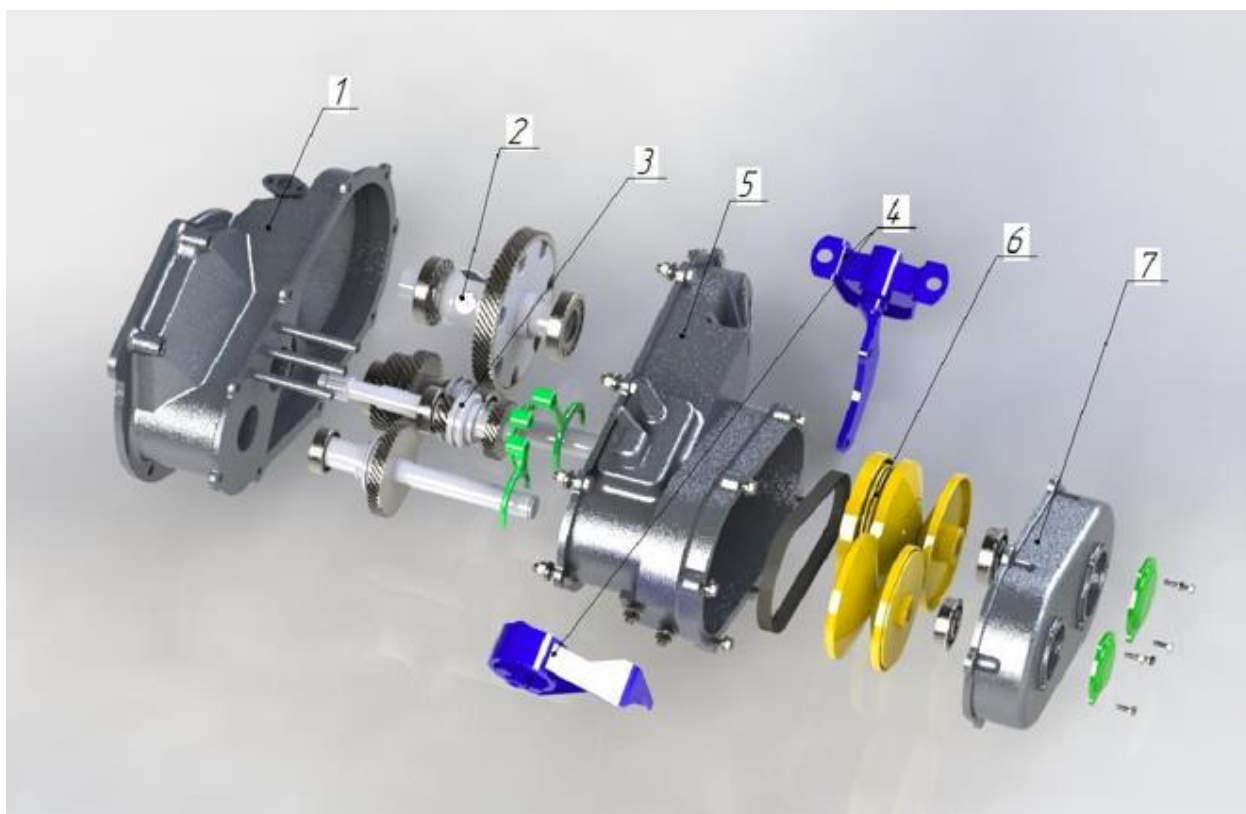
Конструкция коробки передач: 1 – крышка коробки передач; 2 – цилиндрическая главная передача; 3 – механизм реверса вращения; 4 – кронштейны крепления к кузову автомобиля; 5 – корпус вариатора; 6 – клиноременная передача; 7 – крышка клиноременной передачи
